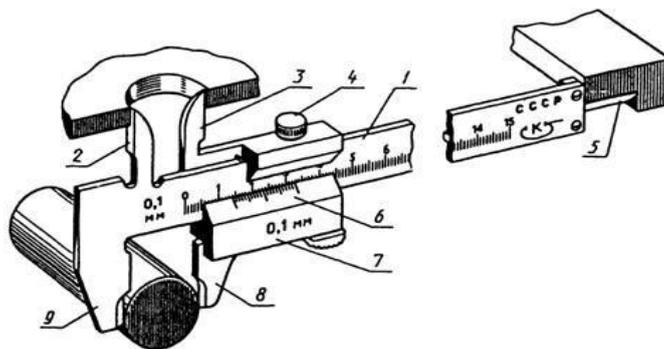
Конструкция штангенциркуля ШЦ-I: 1 – штанга; 2 и 3 – губки для измерения внутренних размеров, 4 – стопорный винт; 5 – линейка глубиномера; 7 – рамка; 6 – нониус; 8 и 9 – губки для измерения наружных размеров
